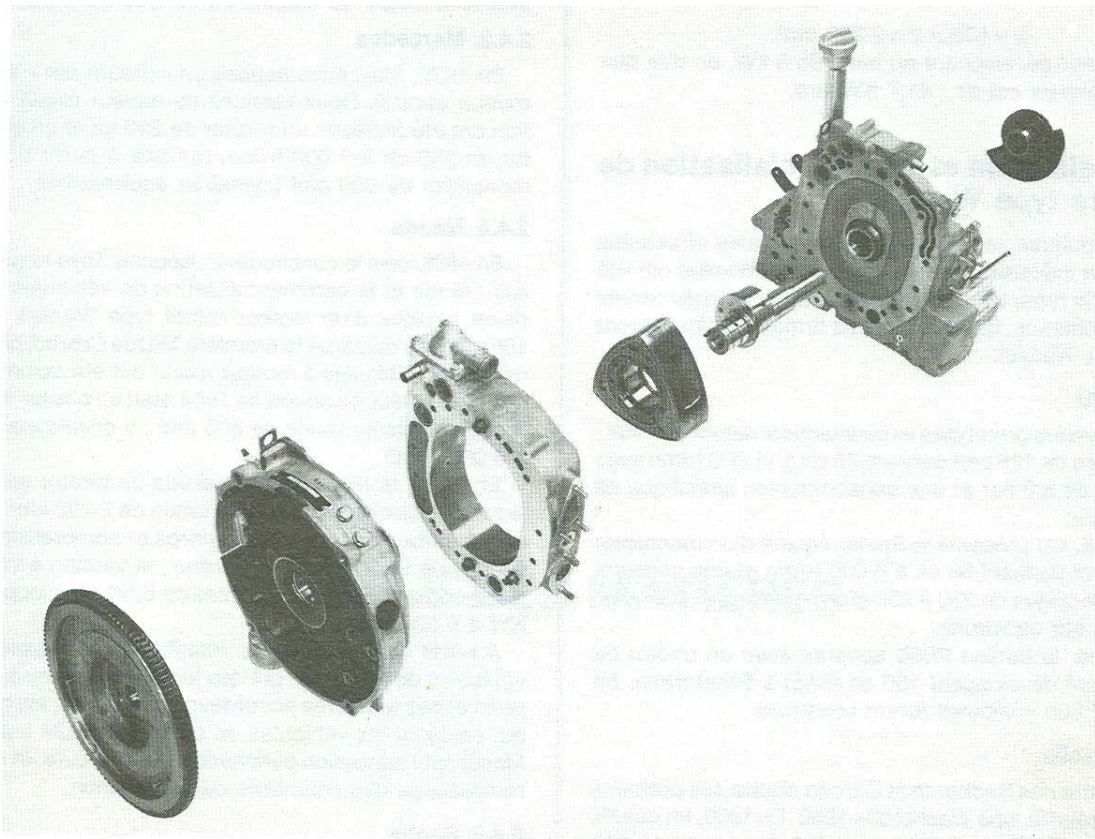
Vue éclatée du moteur Wankel monocylindre
